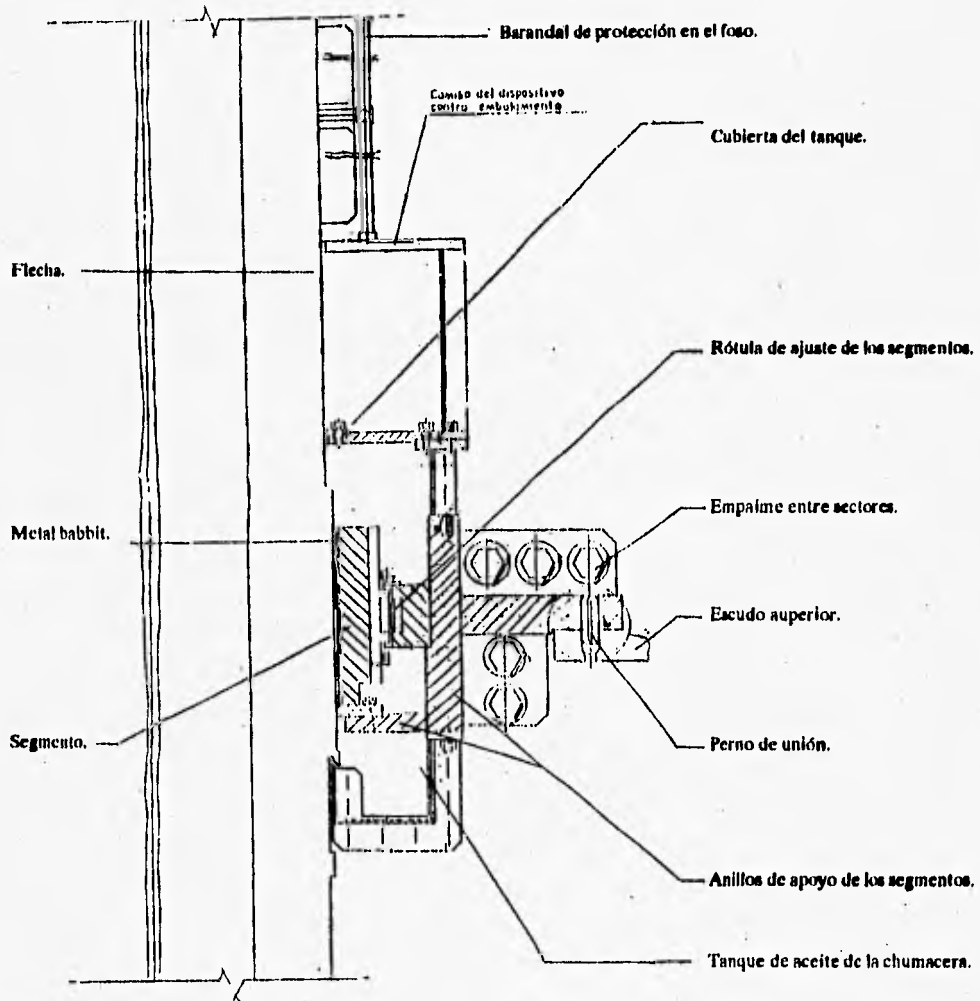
A VISTA EN PLANTA DE LA CHUMACERA GUÍA.
